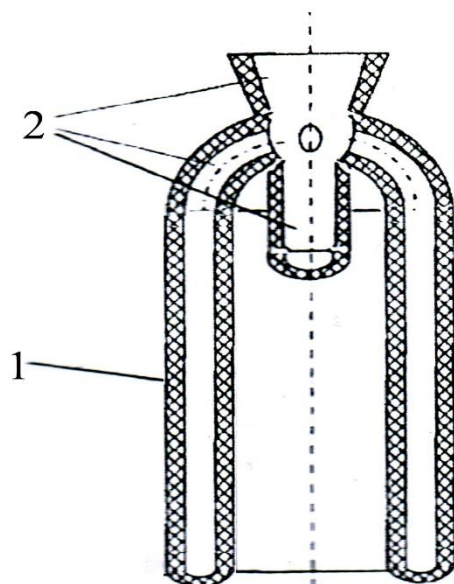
Схема керамічної оболонкової форми для відливки трубчатих заготовок: 1- циліндрична оболонкова частина; 2 — литниково-живільна система з заливною чашею [188]
